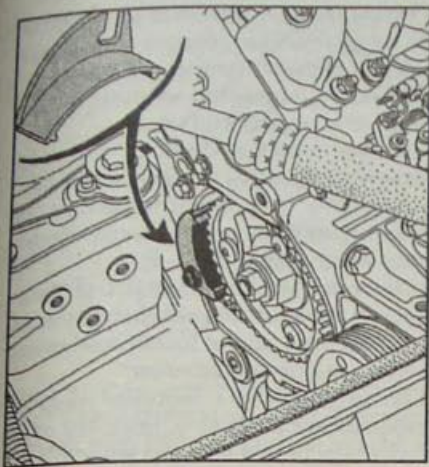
Установка приспособления Mot. 1317 на шкиве топливного насоса высокого давления
